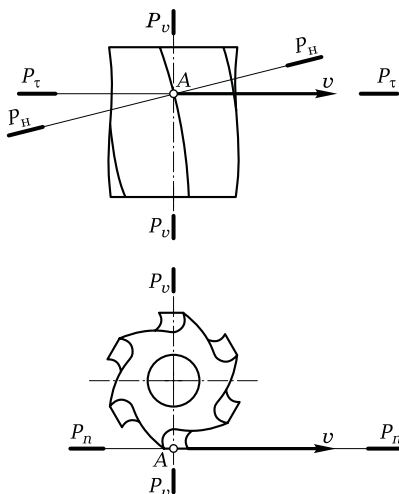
Координатные плоскости при фрезеровании цилиндрической фрезой в статической системе координат:
